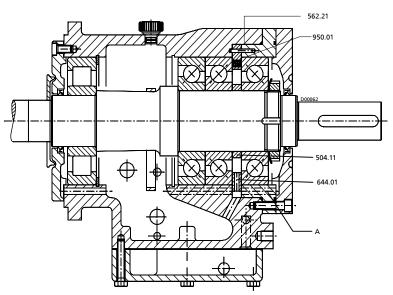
Установка подшипникового узла по схеме "тандем"
